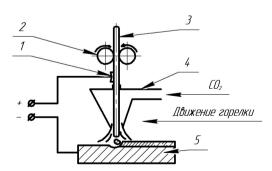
Схема сварки (наплавки) в углекислом газе:
